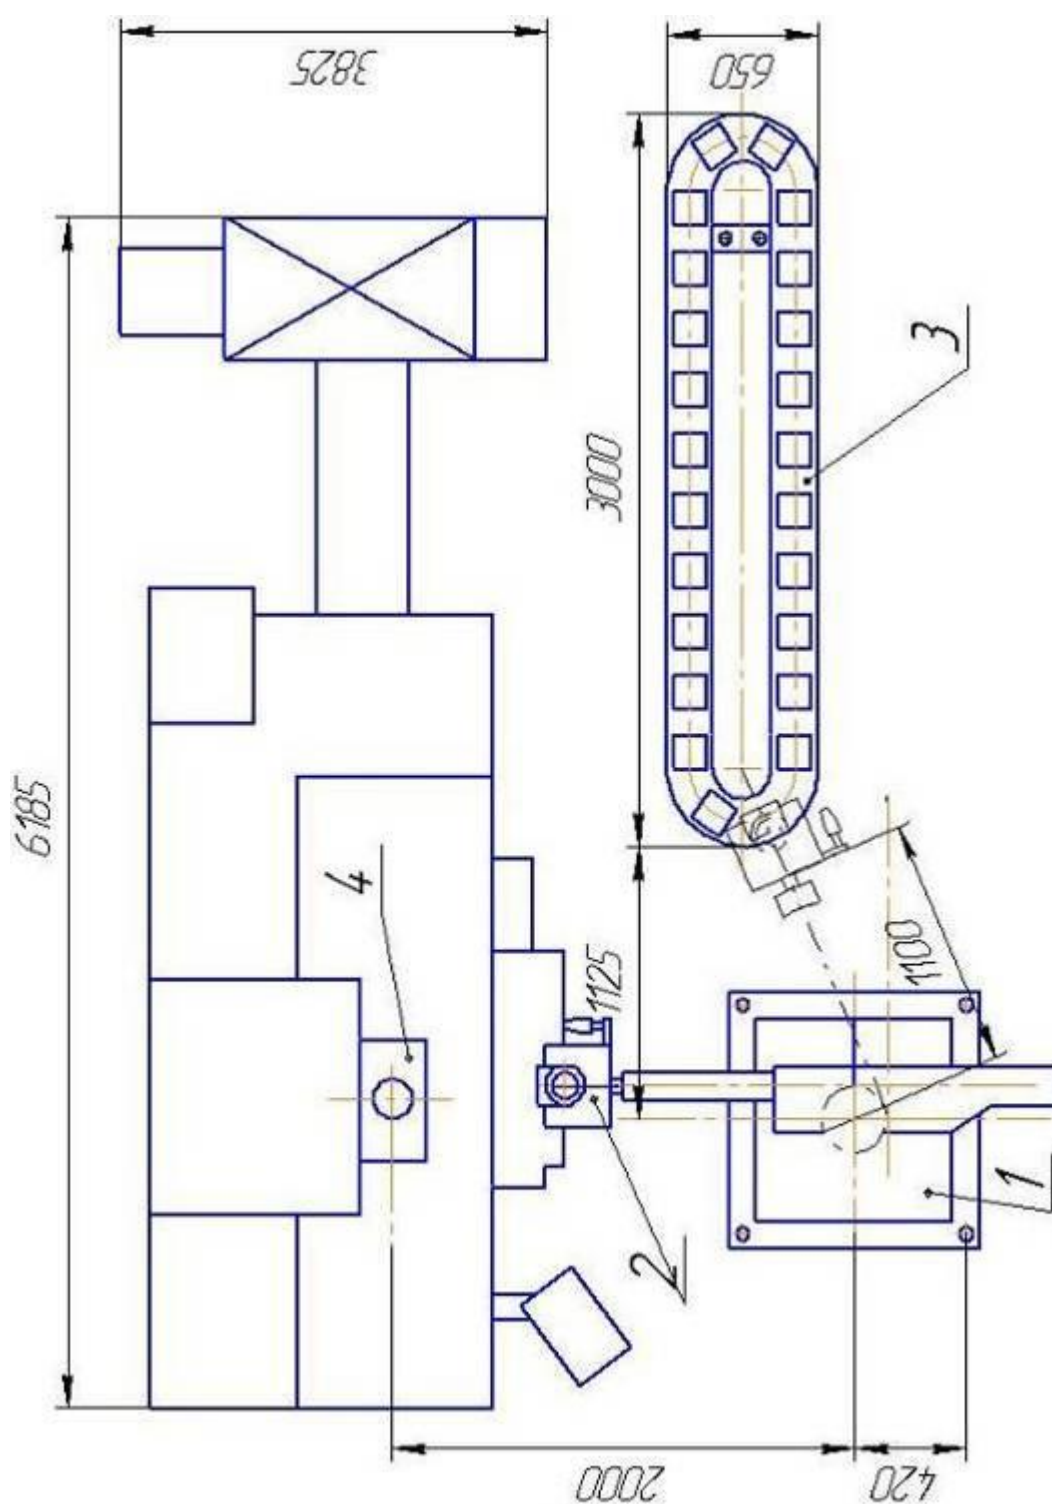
Запропонована РТК компоновка на базі фрезерного верстата моделі 65А60Ф4 - 11
